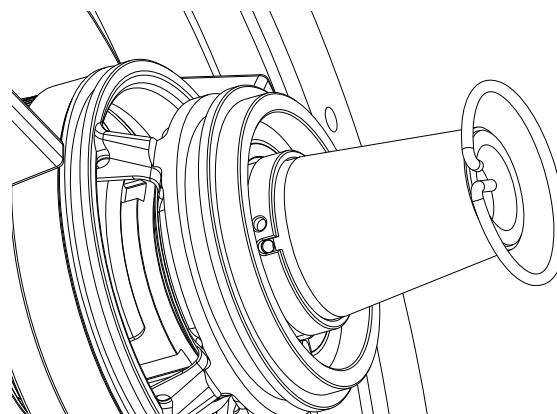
Сборка уплотнения вала, стопорное кольцо
